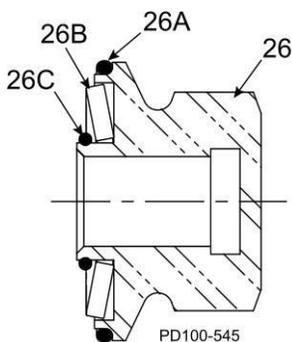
Vue en coupe de l'ensemble écrou de rotor, tel qu'assemblé
